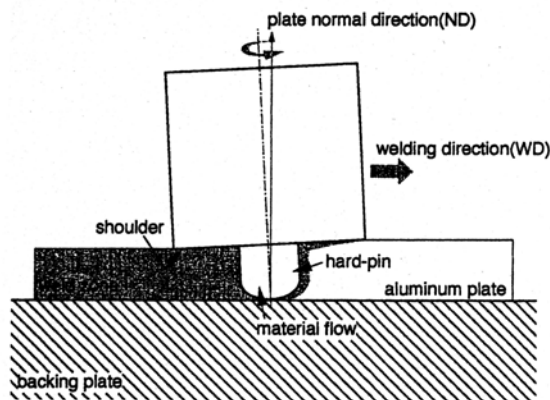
Schémas du procédé FSW : coupe parallèle à la direction de soudage [Sato 2001a]
